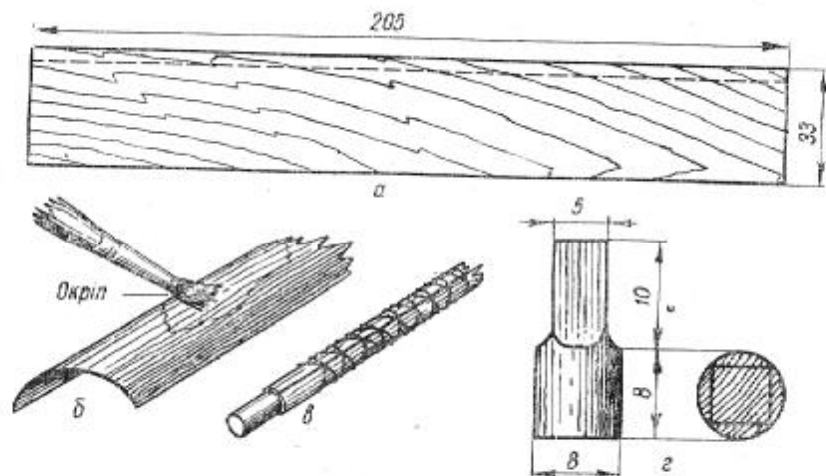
Виготовлення шпонового фюзеляжу з липовими чопами:
